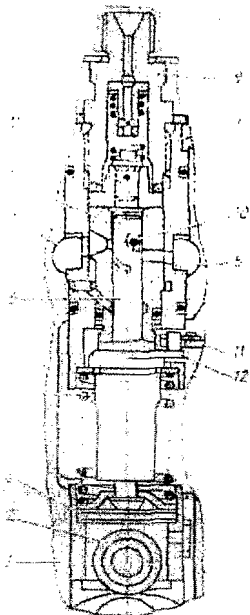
Секция топливного насоса высокого давления: А - полость нагнетания топливного насоса; Б - полость отсеки; 1 - корпус насоса; 2 - толкатель секции; 3 - пята толкателя; 4 - пружина; 5 - плунжер; 6 - втулка плунжера; 7 - нагнетательный клапан; 8 - штуцер; 9 - корпус секции; 10 - отсечная кромка винтовой канавки плунжера; 11 - рейка; 12 - поворотная втулка плунжера
